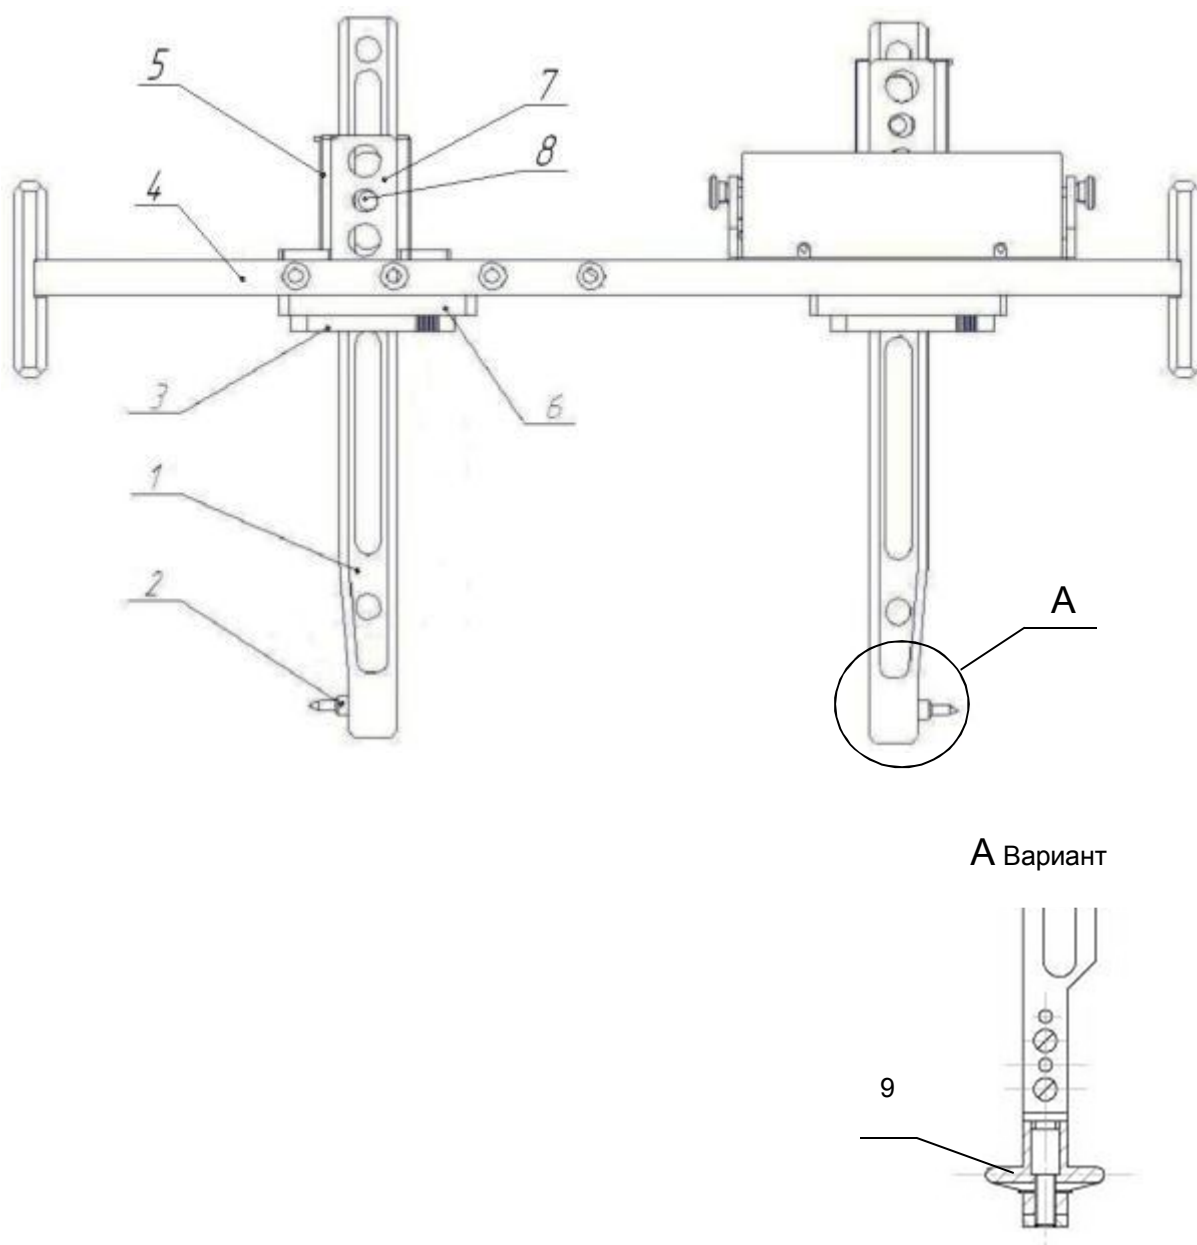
Типовая конструкция индикаторного прибора со ступенчатыми сдвижными упорами и регулируемым по вылету штангами для измерения диаметра уплотнительной расточки муфты в измерительной плоскости и конусности уплотнительной расточки: 1 – штанга; 2 – наконечник; 3 – упор; 4 – траверса; 5 – колодка; 6 – опорная планка; 7 – прижим; 8 – винт; 9 – ролик (применяется при измерении муфт большого диаметра).
